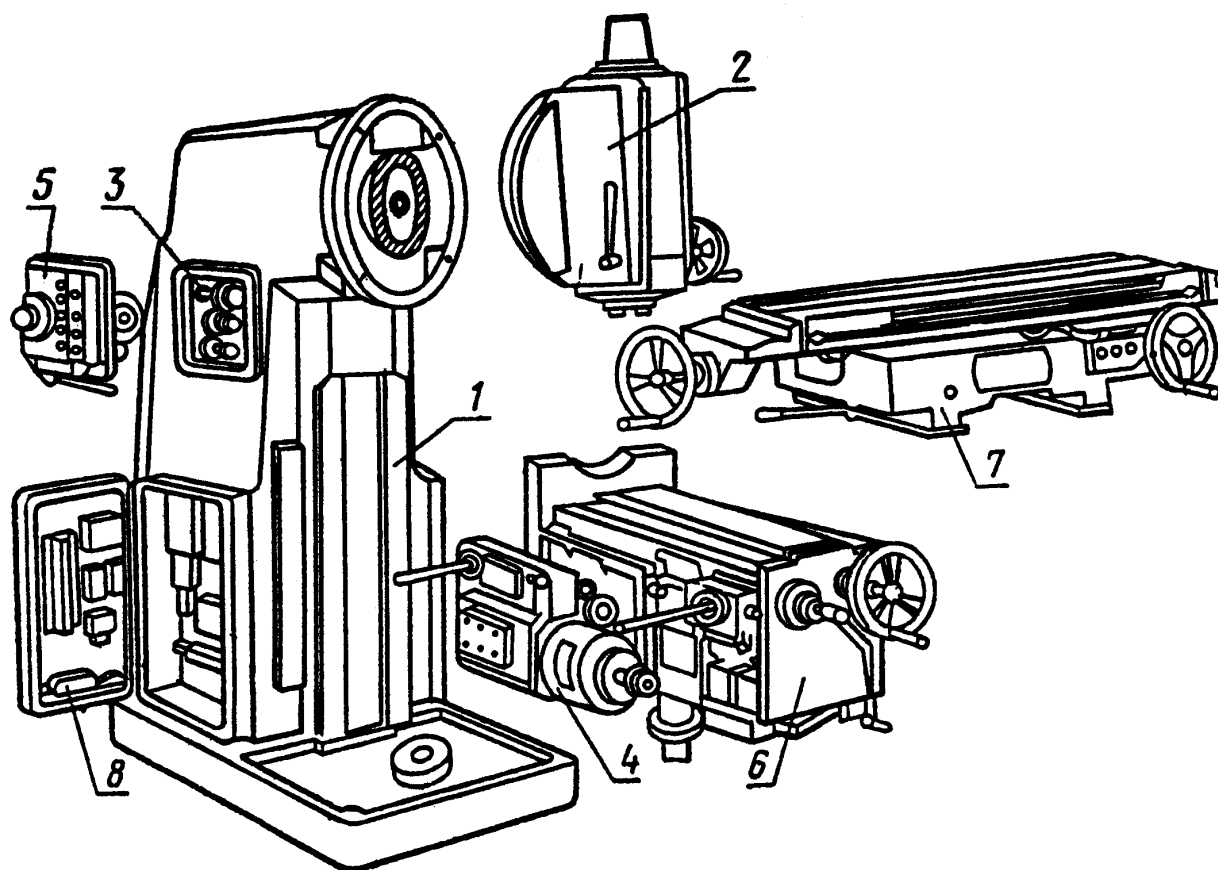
Схема расчленения консольно-фрезерного станка на сборочные единицы: 1 – станина в сборе; 2 – поворотная головка; 3 – коробка скоростей; 4 – коробка подач; 5 – консоль; 6 – стол и салазки; 7– электрооборудование
